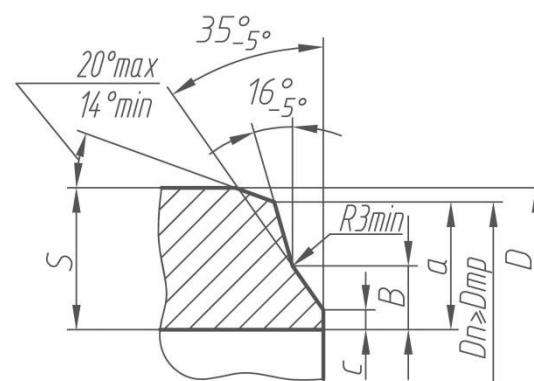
, лист 2 – Типы механической обработки кромок патрубков (приварных катушек, ответных фланцев) с наружным диаметром, равным диаметру присоединяемой трубы
